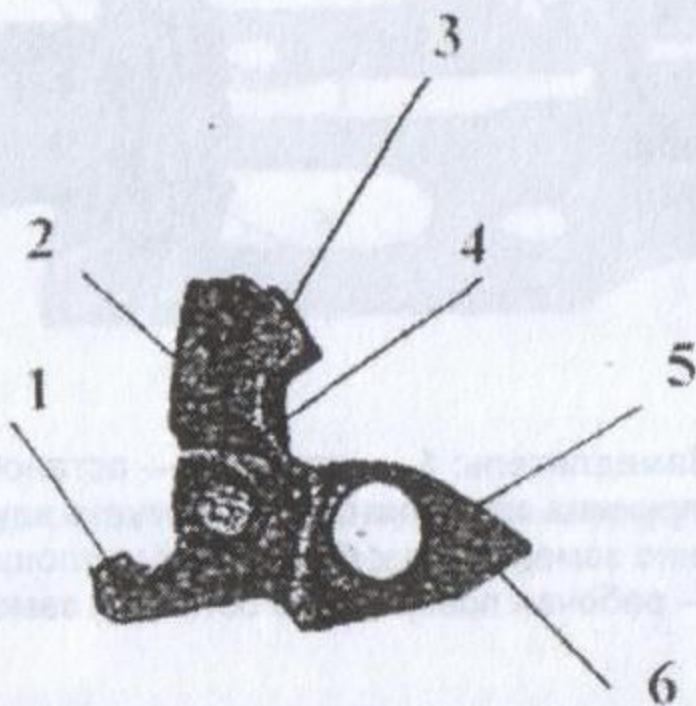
Шептало: 1 — хвостовик шептала; 2 — щека шептала правая; 3 — зацеп шептала; 4 — щека шептала левая; 5 — плечо; 6 — собственно шептало
